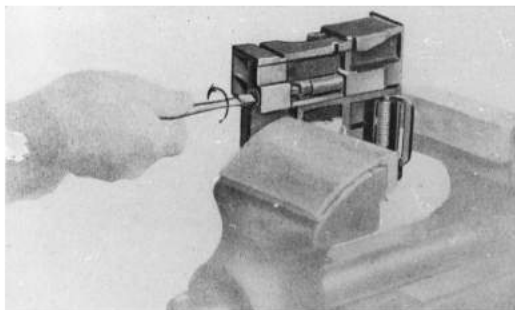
Gesamt-Zerlegung der Waffe: Abschrauben der Führungsstangen für die Zubringerfedern
